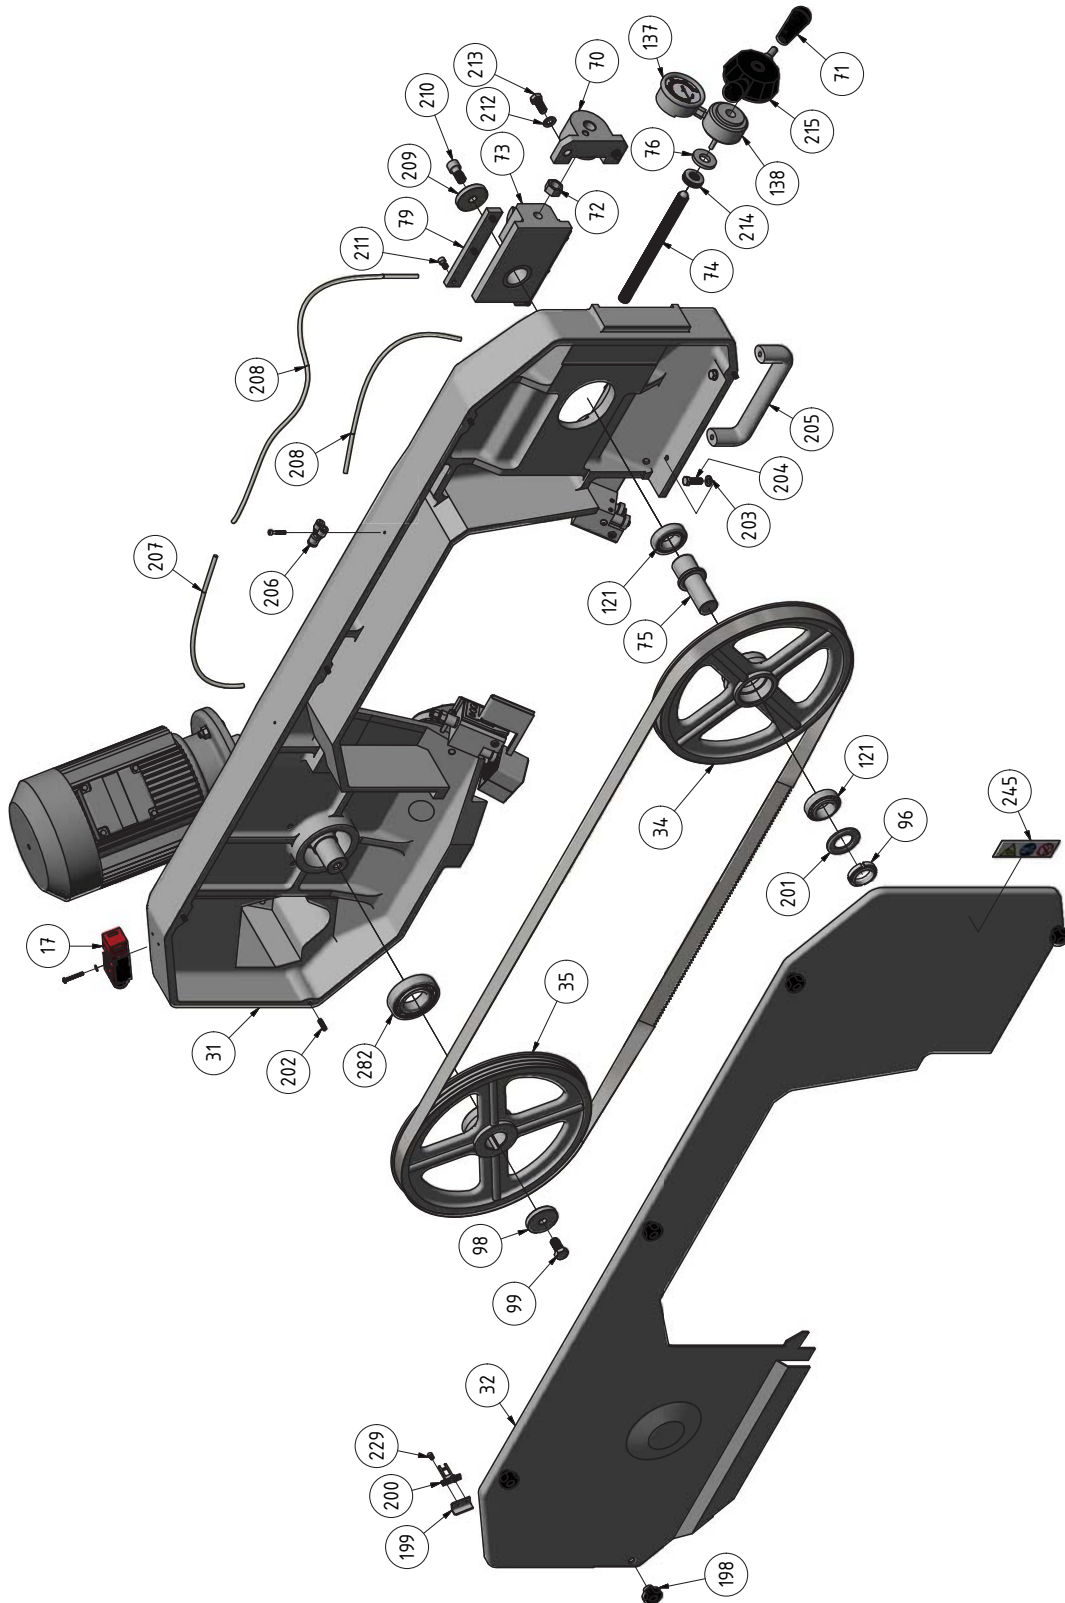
Explosionszeichnung - Drawing spare parts
